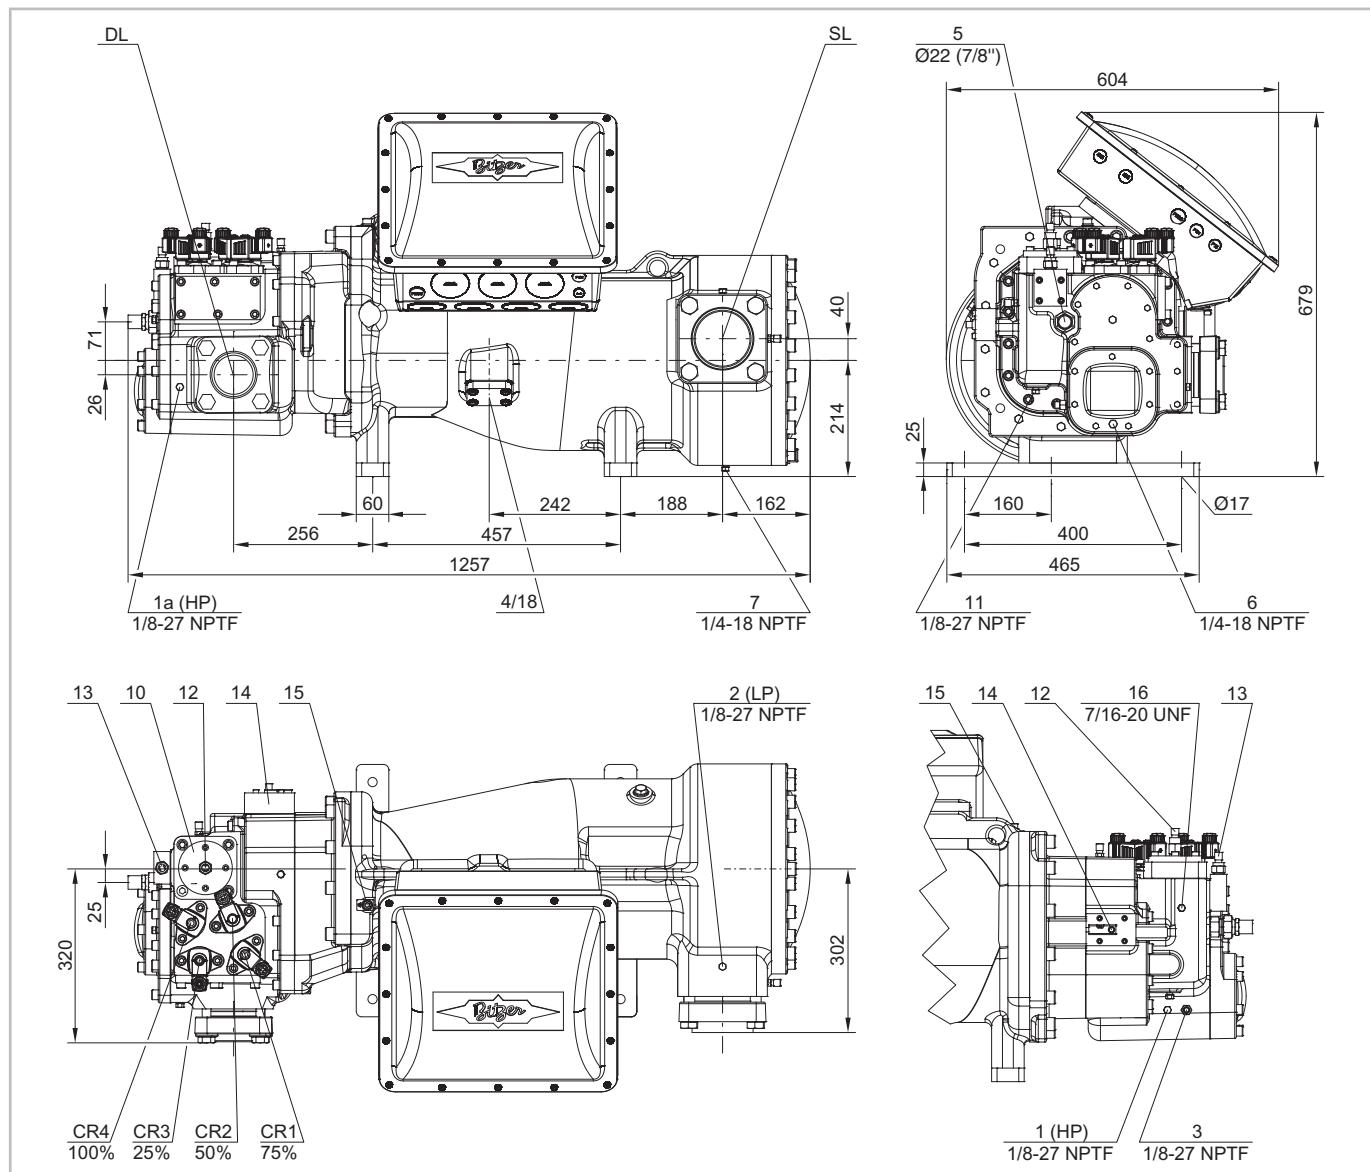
Maßzeichnung HS.8551 .. HS.8571
